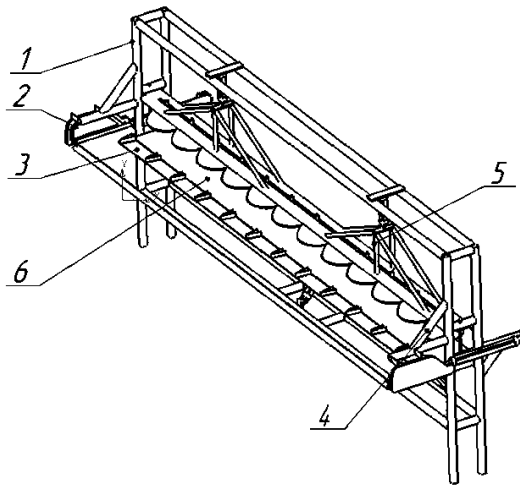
Апарат для вакуумного охолодження хлібобулочних і кондитерських борошняних виробів із завантажувальним пристроєм: 1 — рама; 2 — захватний пристрій; 3 — напрямні; 4 — вакуум-камери; 5 — підйомно-опускний механізм; 6 — вивантажувальний пристрій
